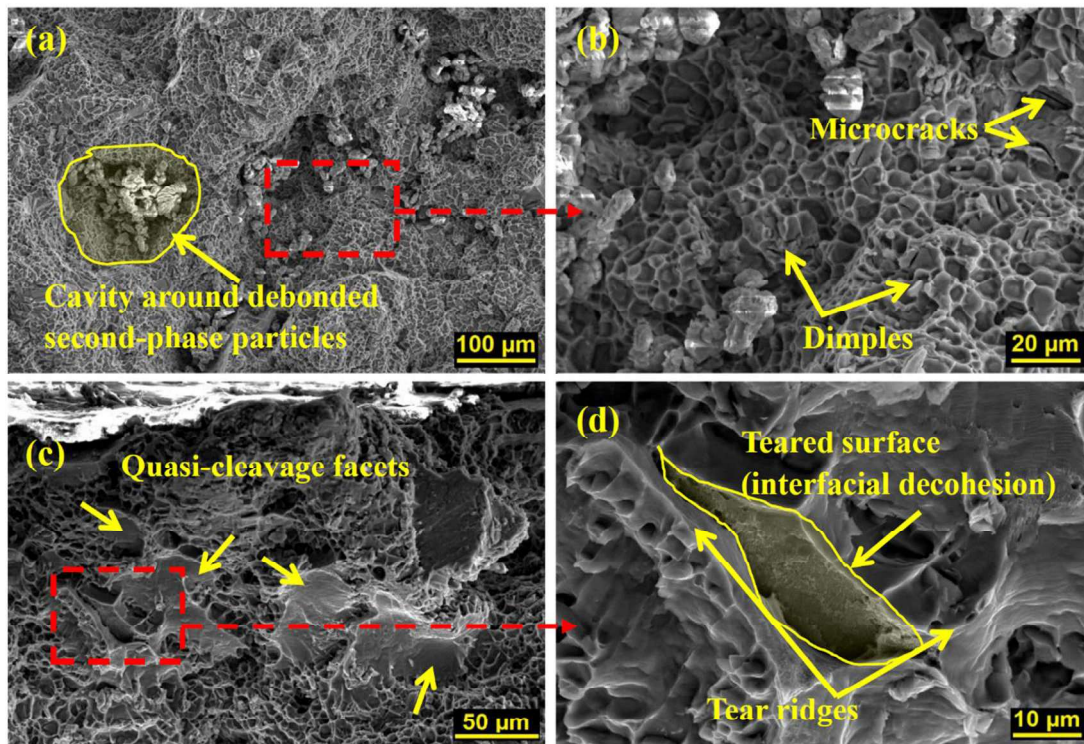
Micrografie SEM delle superfici di frattura (a, b) del campione testata motore non caricato a diversi ingrandimenti e (c, d) del campione testata motore caricato a diversi ingrandimenti [24].
